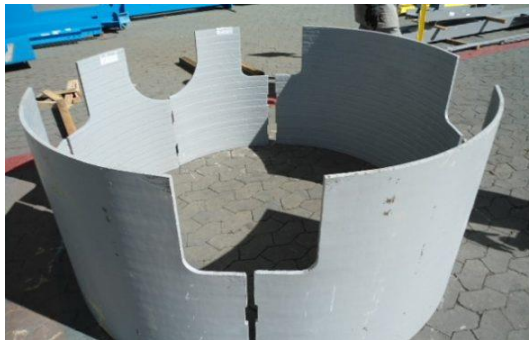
Chapa de revestimento fabricada em ferro fundido branco
